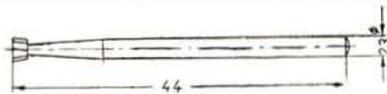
Bohrer, lange Form (Maßstab 1 : 1)
